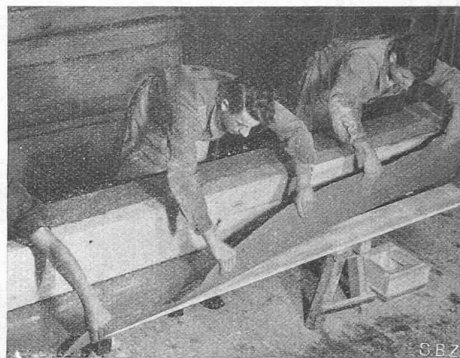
Moulage d'un canal de ventilation sur un mandrin intérieur.
